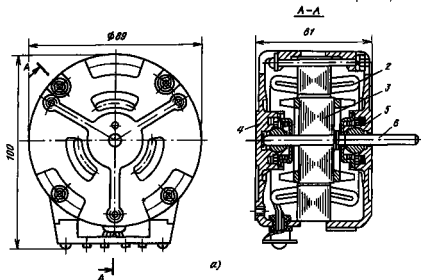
10 Асинхронный конденсаторный двигатель КД-6-4 с фиксацией подшипникового цента
